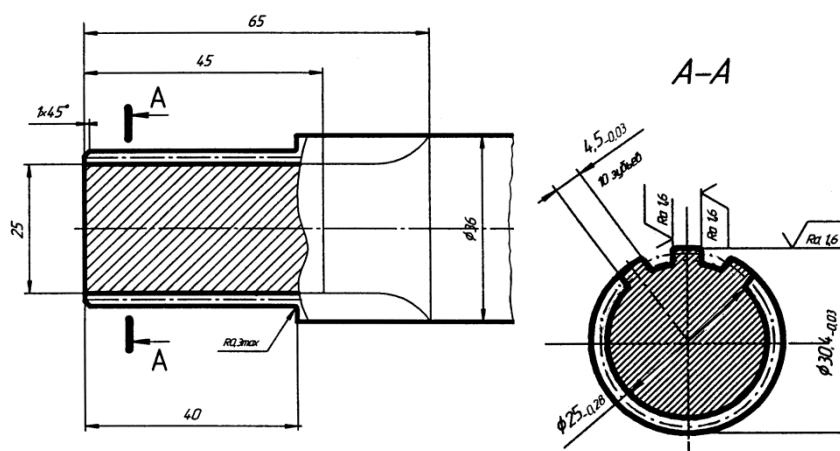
Прямобочные шлицы вала редуктора рулевого управления.
